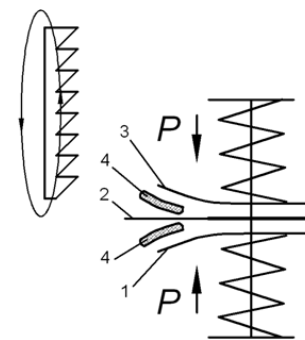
Механізм переміщення матеріалів із зубчатою рейкою та пневматичним пристроєм:
